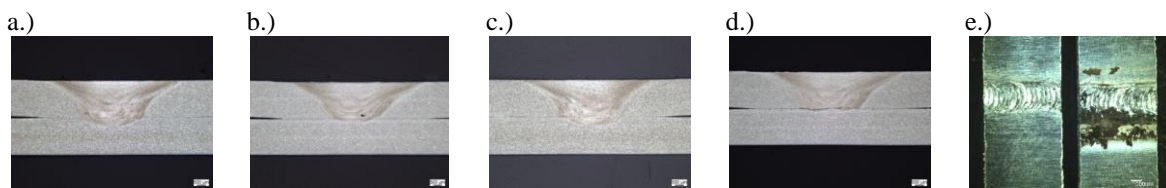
Validierung der Einbringung von Unregelmäßigkeiten beim Schweißen von Stumpfstößen: a.) i.O.-Naht; b.) verkürzter Schweißstift; c.) Maschinenfett in Schweißzone; d.) Maschinenfett in Schweißzone und verkürzter Pin; e.) Papier in Schweißzone
